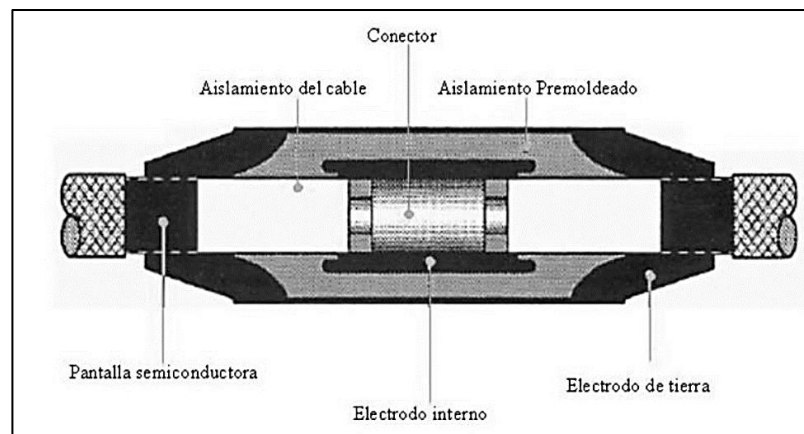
17 *Empalme premoldeado de una pieza - partes.
